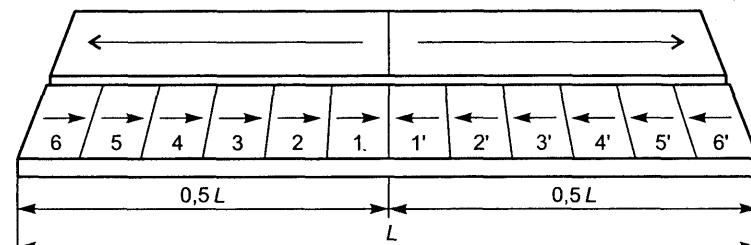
Сварка обратноступенчатым способом от середины к краям
